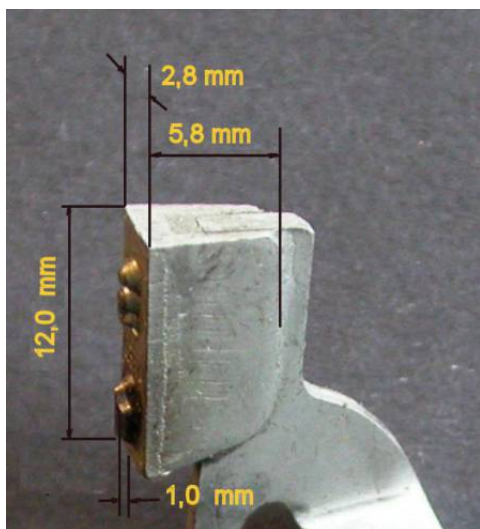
Maße einer Stahl-Zifferntype, hier auf einem Typenhebel einer Schreibmaschine aufgelötet.
